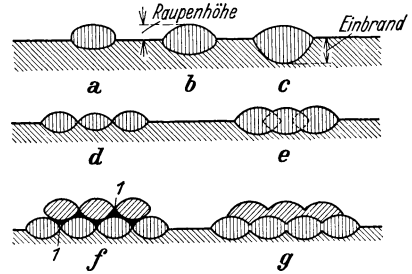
Querschnitte durch Schweißraupen.
